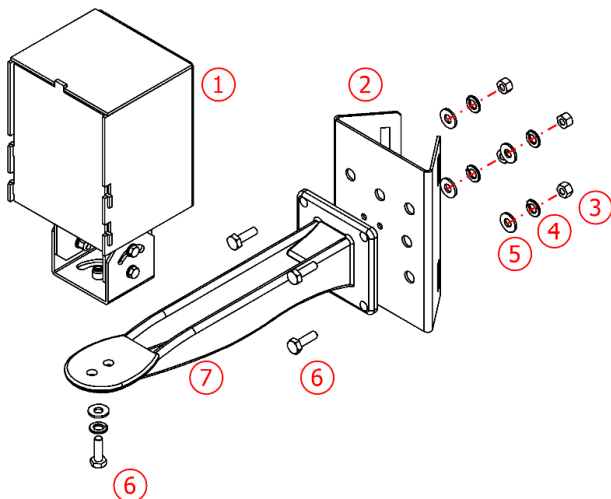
Piezas del soporte de la celda del iluminador ITSLUX
